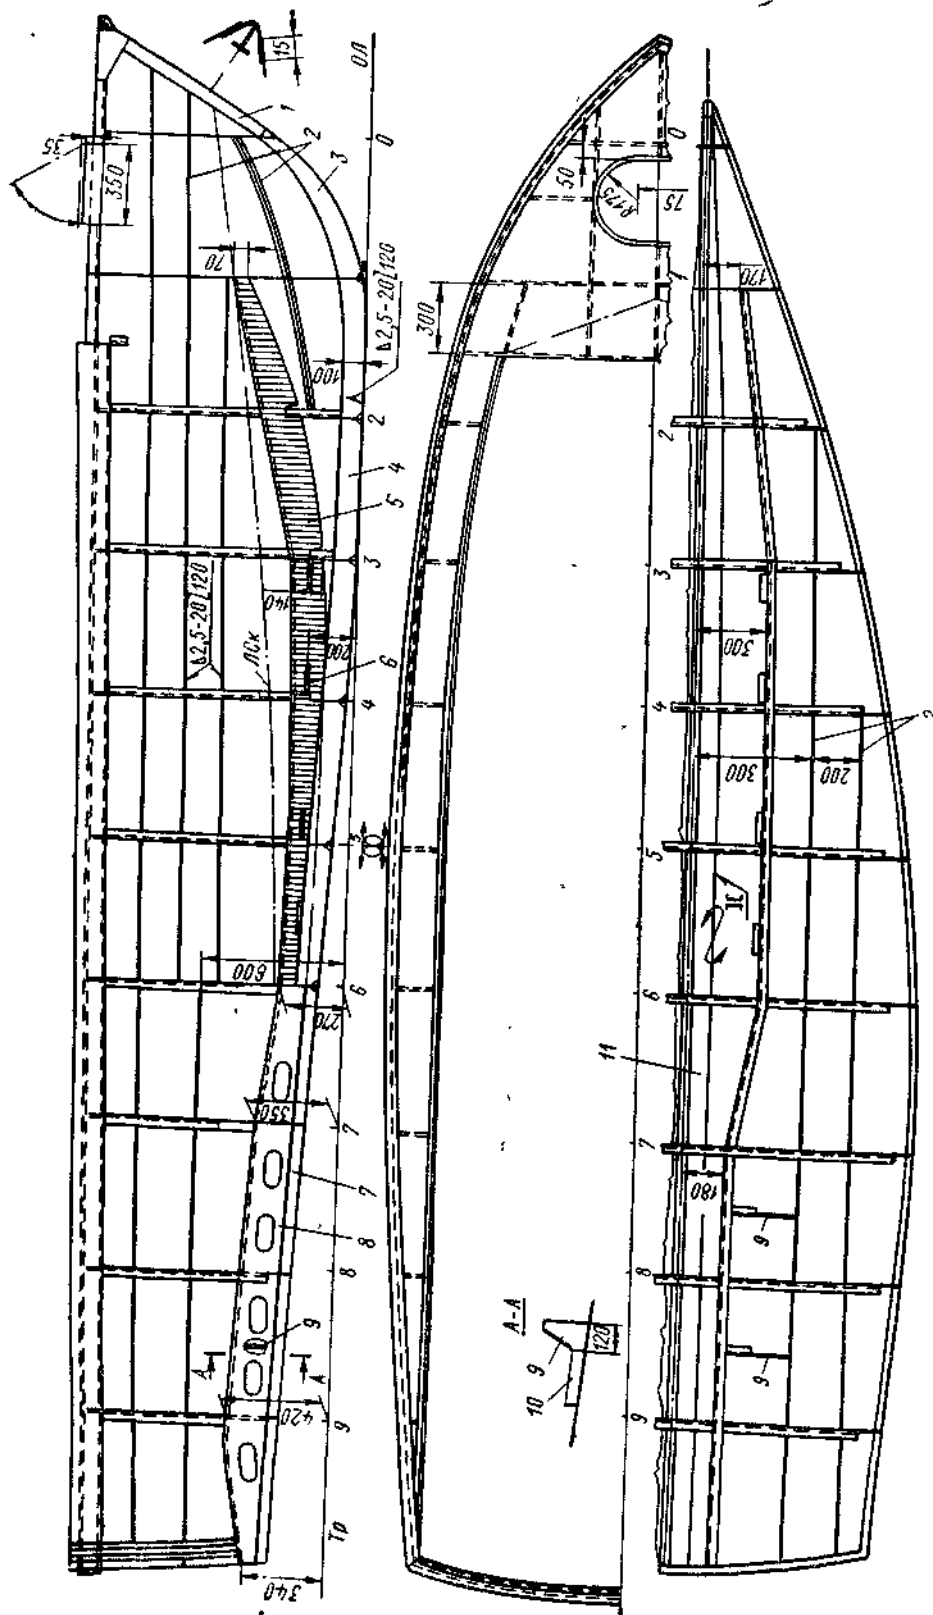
Конструктивный чертеж стального корпуса сварной конструкции.
